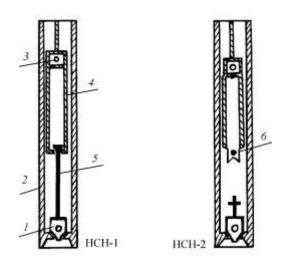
Невставные скважинные насосы: 1 – всасывающий клапан; 2 – цилиндр; 3 – нагнетательный клапан; 4 – плунжер; 5 – захватный шток; 6 – ловитель
